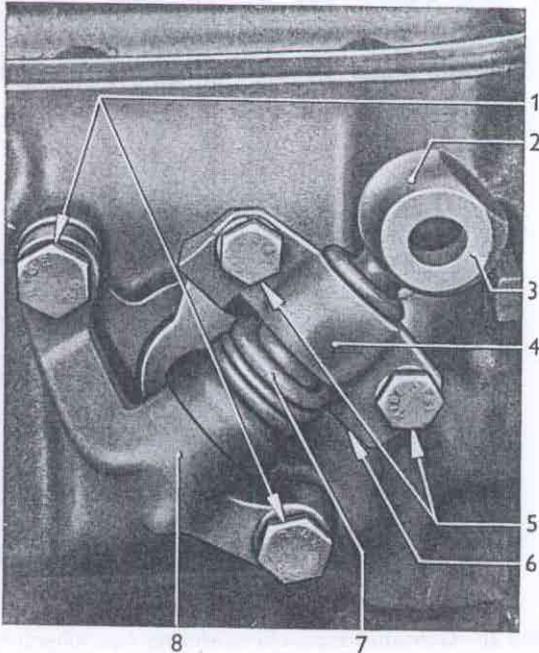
Getriebegelegenkebel an Getriebschaltwelle
